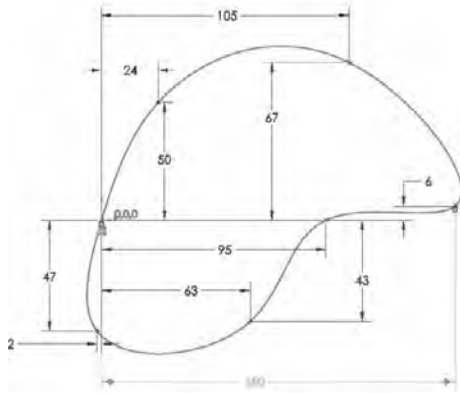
figura construida en MMGS en este caso el plano de trabajo es planta con el fin de realizar el diseño de la forma más sencilla.
